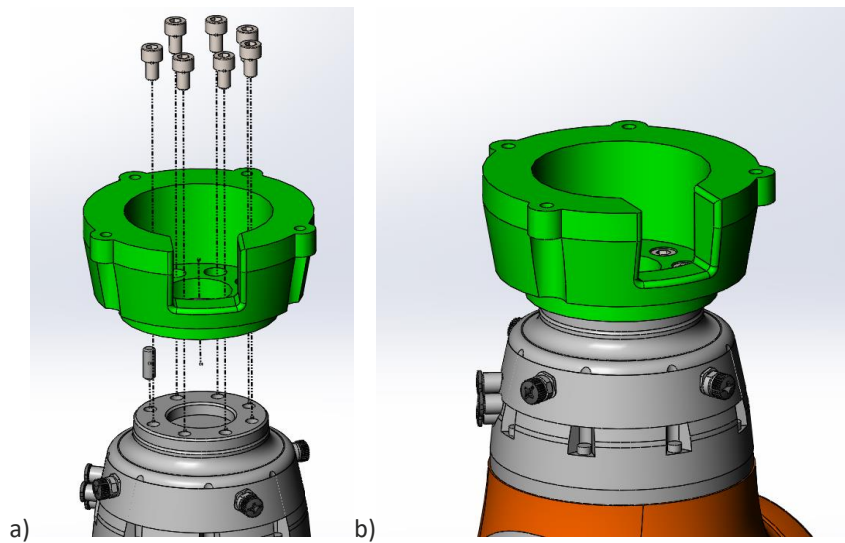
1ª parte da montagem - vista explodida da montagem (a) e parte da montagem completa (b).
